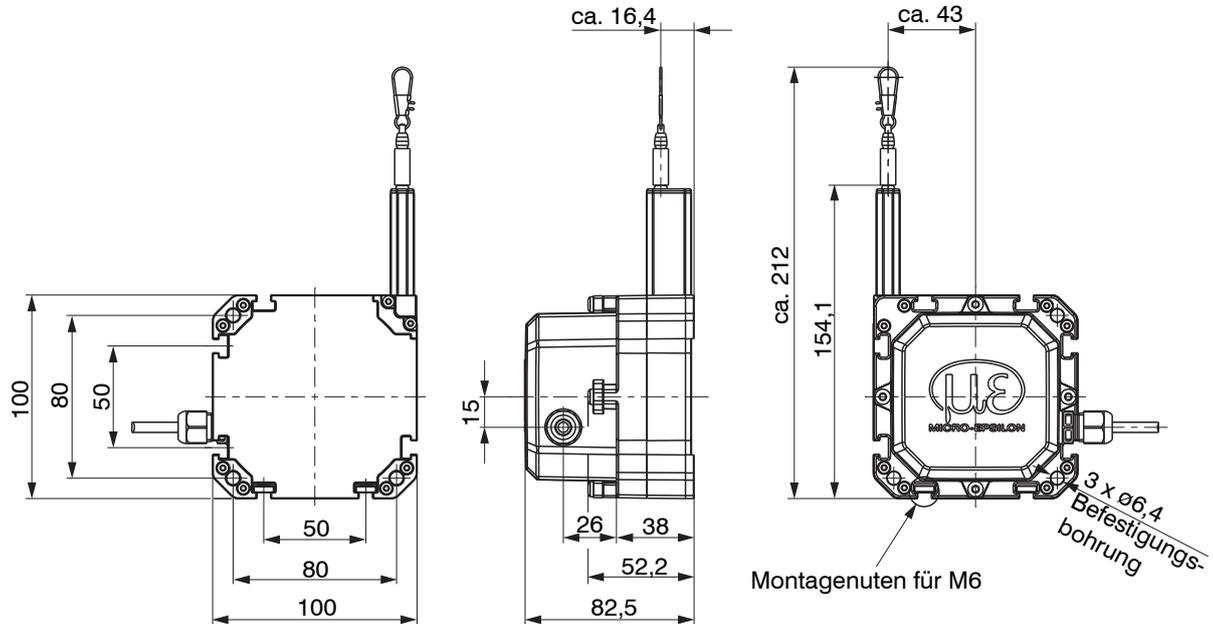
Maßzeichnung WPS-3500-K100, WPS-5000-K100, WPS-8000-K100 mit integriertem Kabel, radial, Länge 1 m, Abmessungen in mm
